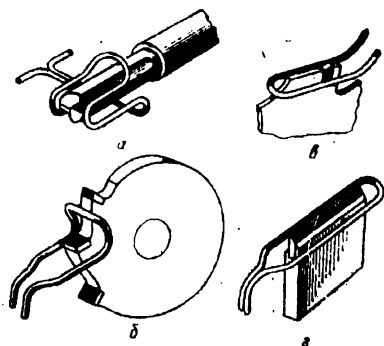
Формы индукторов для напайки ТВЧ пластинок твердого сплава:
